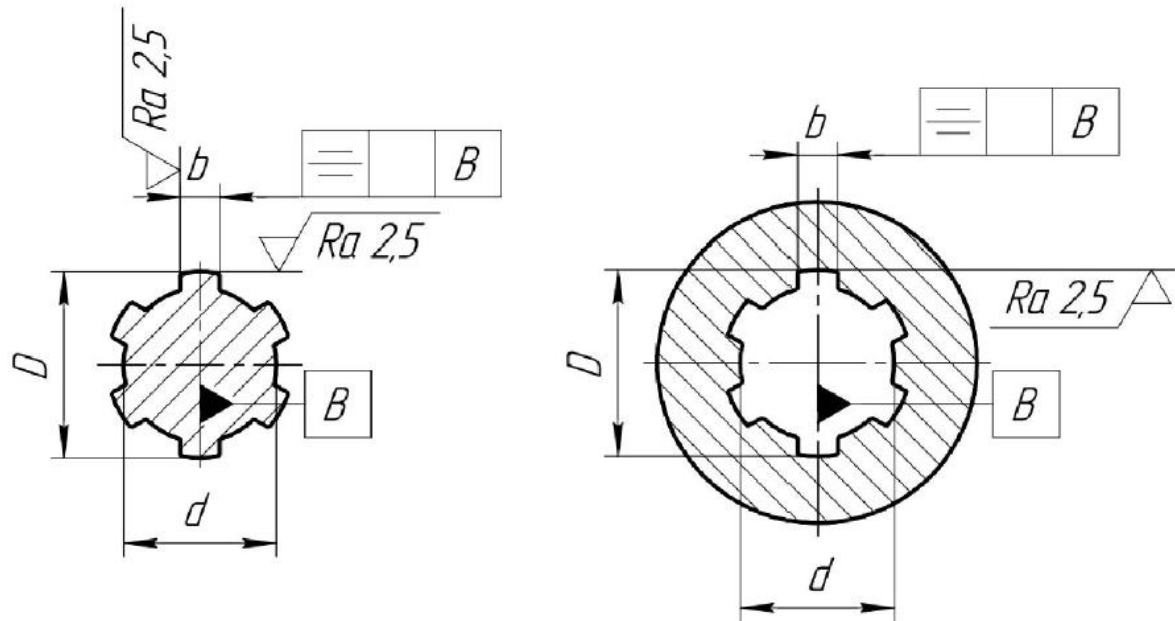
Базові поверхні, чистота обробки та допуски форм і розташування поверхонь шліцевого прямобічного з'єднання при центруванні по бічних сторонах
